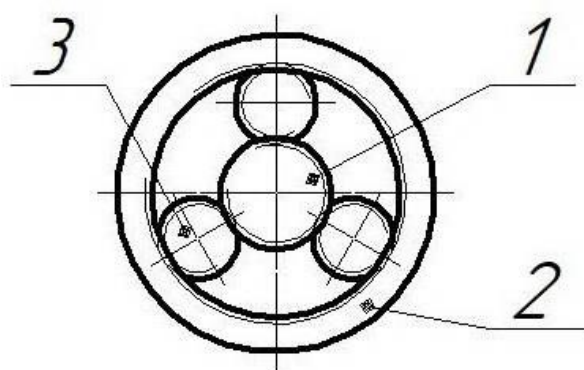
Схема передачи с цилиндрическими резьбовыми роликами:
